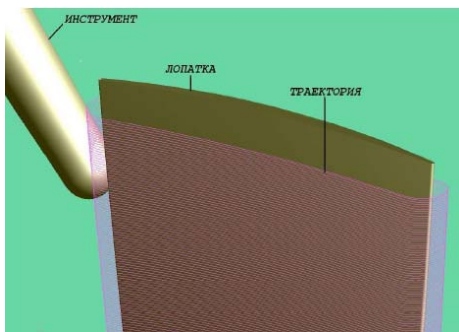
Формообразование пера лопатки спиральным высокоскоростным фрезерованием
